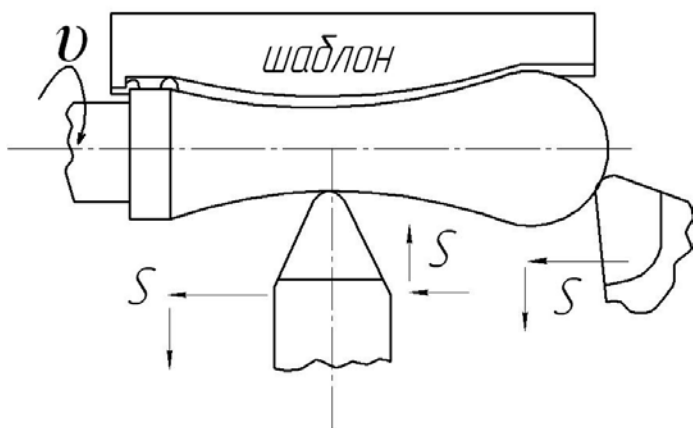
Схема обработки неточной длиной фасонной поверхности
